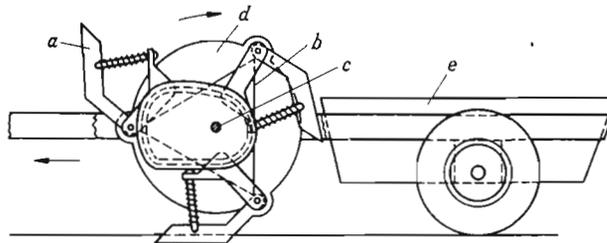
Steinsammelmaschine mit intermittierend angetriebener Zinkengabel
